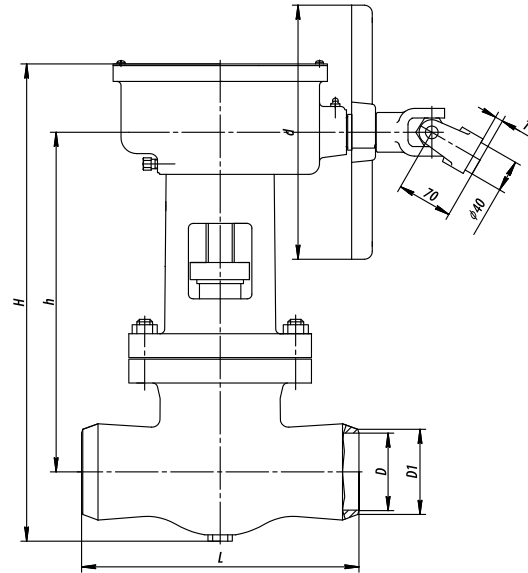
Задвижка DN80-100 с коническим редуктором
